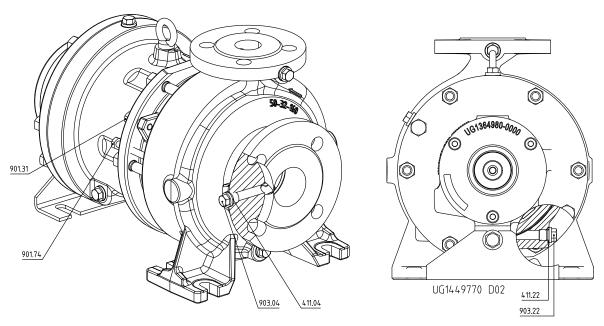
Крепление крышки с напорной стороны на корпусе насоса для исполнения с зажимной крышкой Варианты конструкции
